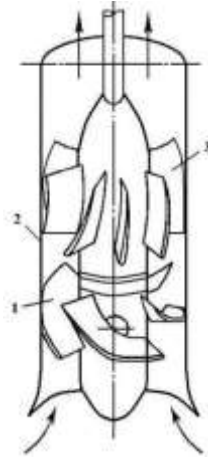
Схема пропелерного насоса: 1 – робоче колесо; 2 – корпус; 3 – направляючий апарат
